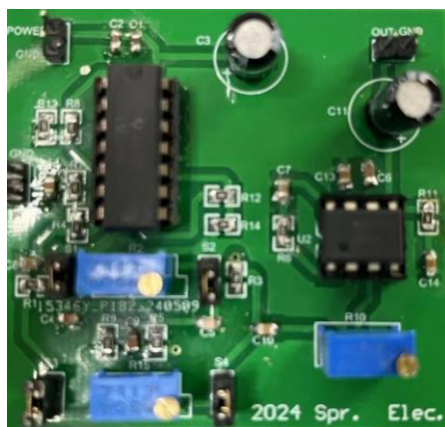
音频放大器系统 PCB 电路板焊接实物图
